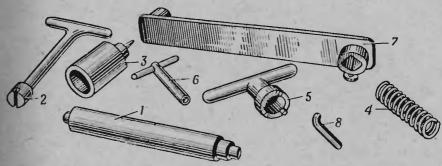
Орудийный комплект ЗИП, укладываемый в сверток для инструмента:
